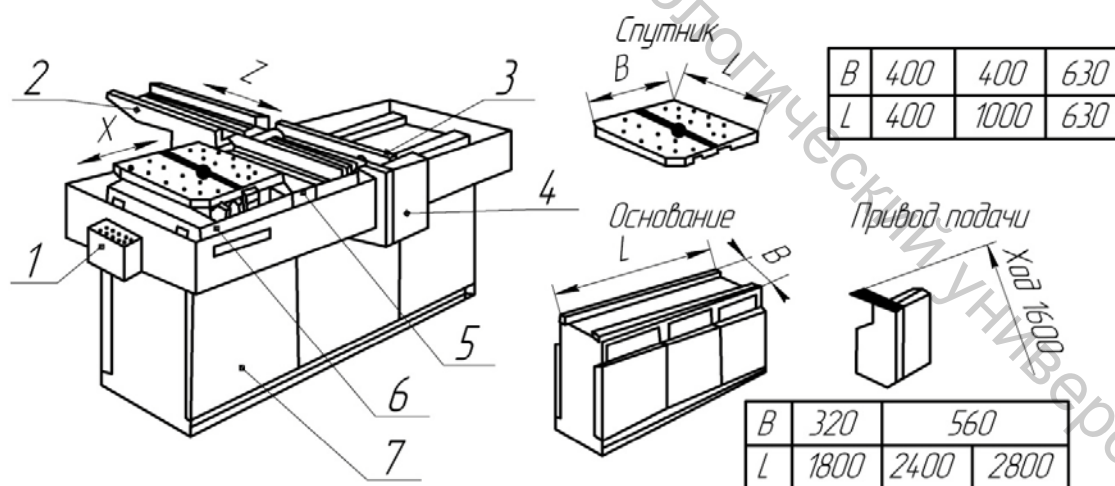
Агрегат загрузки спутников и конструктивные элементы
